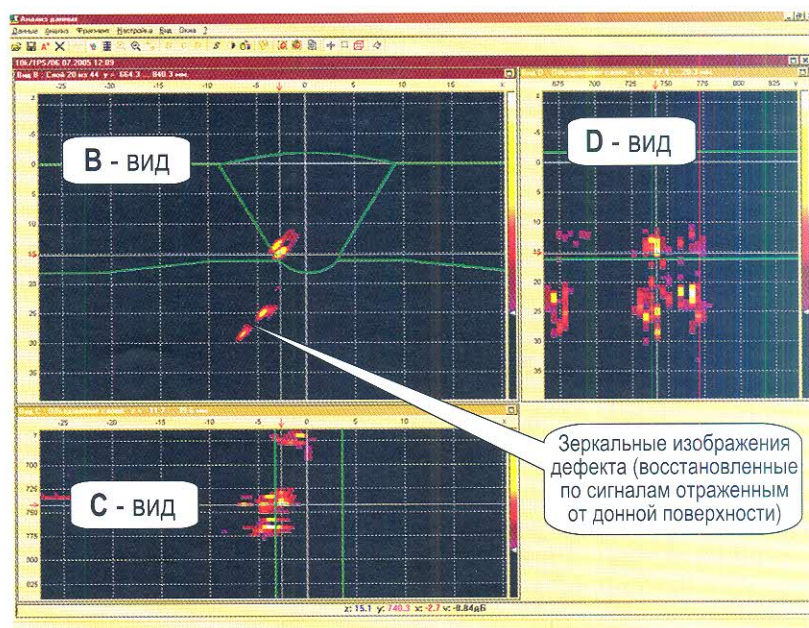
Три сечения (вида) трехмерного изображения двух плоскостных дефектов, расположенных в корне сварных соединений: хорошо видны блики от трещины из корня шва и зеркальные блики, отраженные от верхней части трещины (в нижней части В-вида); линиями обозначены контуры разделки сварного соединения
